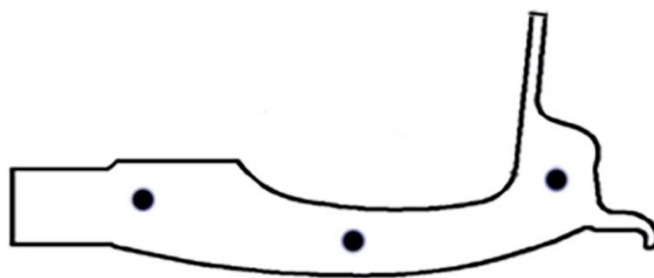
Типовое расположение точек замера твердости в образце колеса
